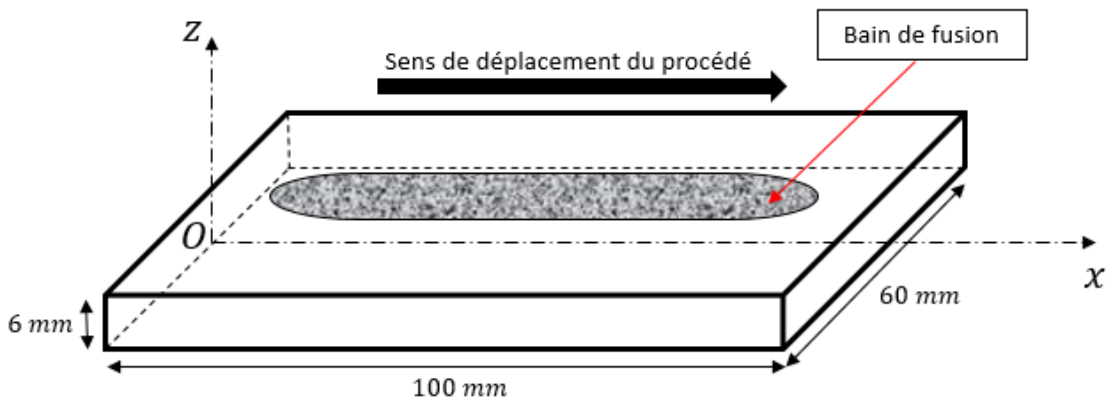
Géométrie du cas test de soudage simple
